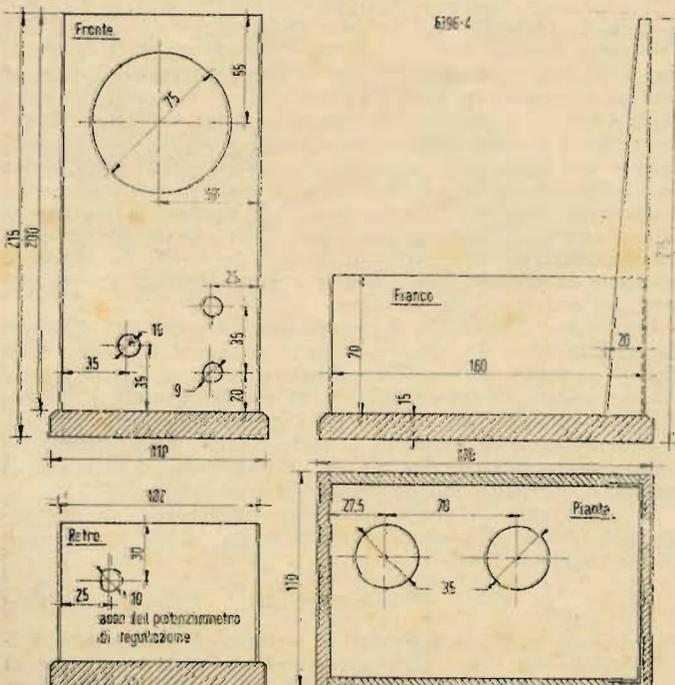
Pianta fronte e profilo del millivoltmetro. Quote in millimetri.
